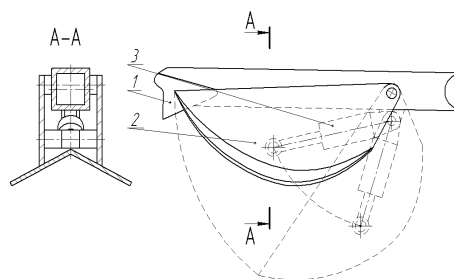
Поворотный упор: 1 – рукоять, 2 – кулачек, 3 – привод кулачка
